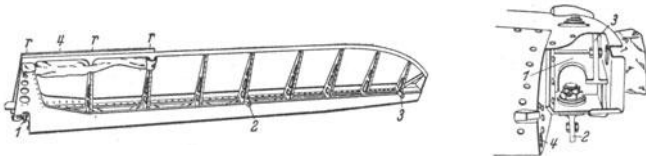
¹⁾. Querruder (unbespannt) des Henschel-Mehrzwecke-Flugzeugs Hs 126 (s. Fig. 19). 1, 2, 3 Lagerstellen des Querruders, 4 Trimmkante (halbhartes Aluminiumblech), 7 Rippen. In der Nebenfigur bedeuten: 1 Beschlag des inneren Ruderlagers (Elektronfuß), 2 Lageranschlußbolzen (Stahl), 3 am Beschlag 1 angegossener Arm für den Anschluß des Betätigungsgestänges, 4 Eintrittsöffnung des Rohres für den genauen Gewichtsausgleich. Dieses Rohr wird mit Stahlkugeln gefüllt. (Das eigentliche Ausgleichgewicht besteht aus einer Stahllange, die mit angeschweißten Lappen an den Querruderrippen befestigt ist.)
